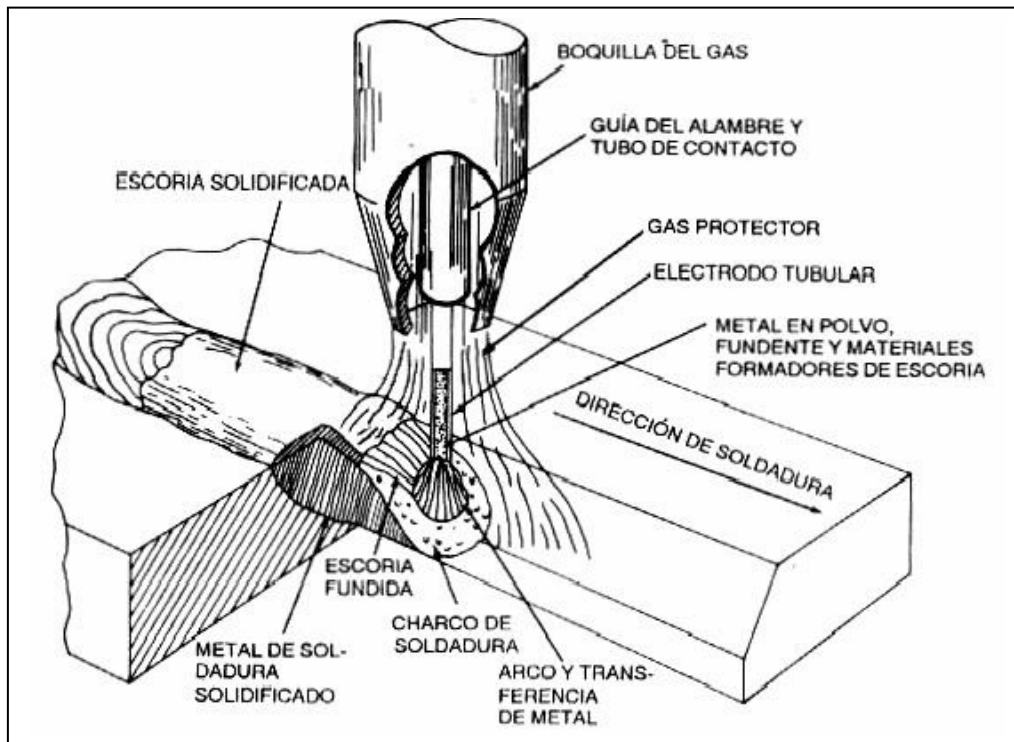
Dibujo esquemático en el que aparecen las distintas nomenclaturas de las partes que conforman la soldadura por arco.
